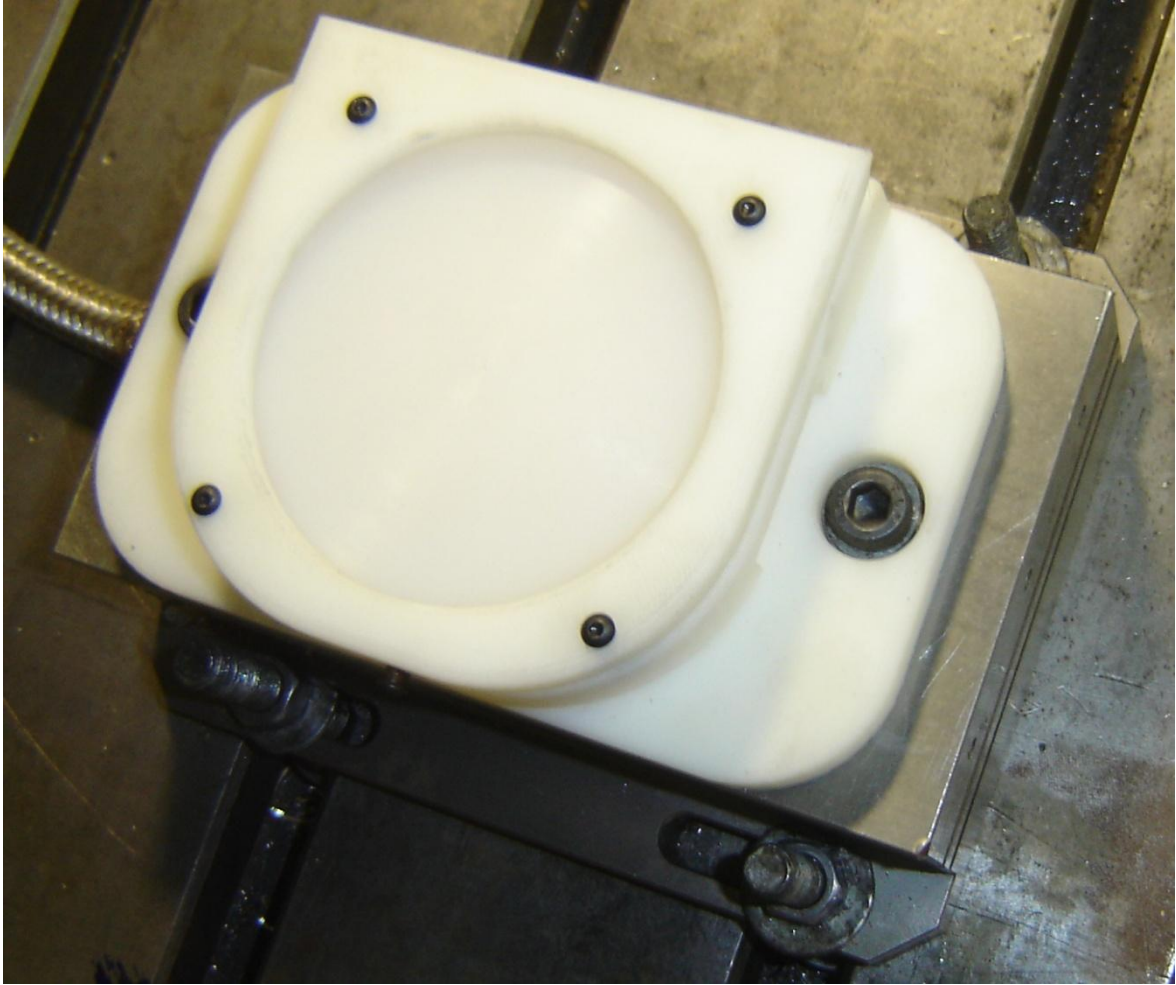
Corpo de prova fixado no suporte sobre o dinamômetro.
